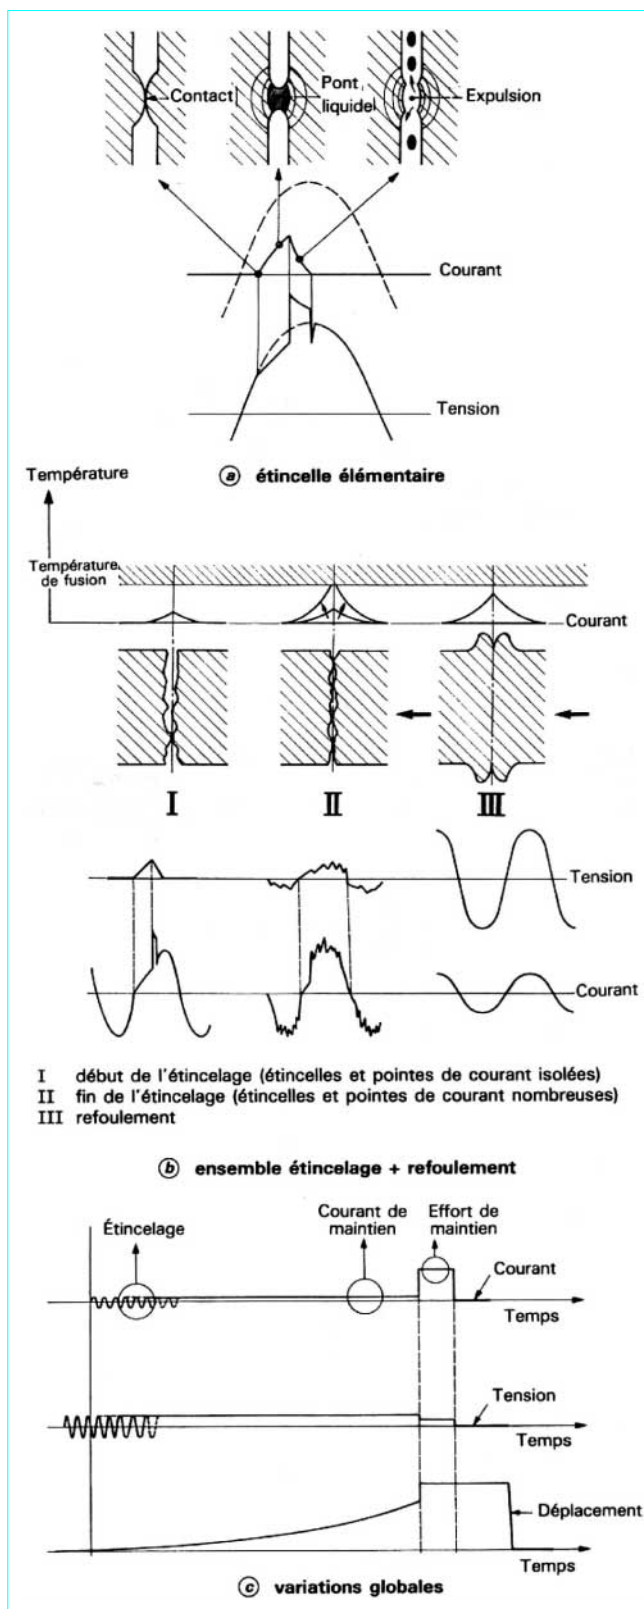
Soudage en bout : formation de la soudure par étincelage en courant alternatif
